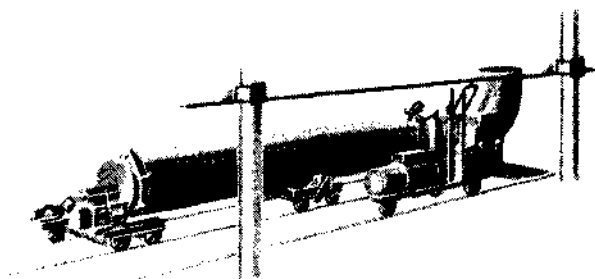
Станок для сварки трубопроводов в среде углекислого газа
